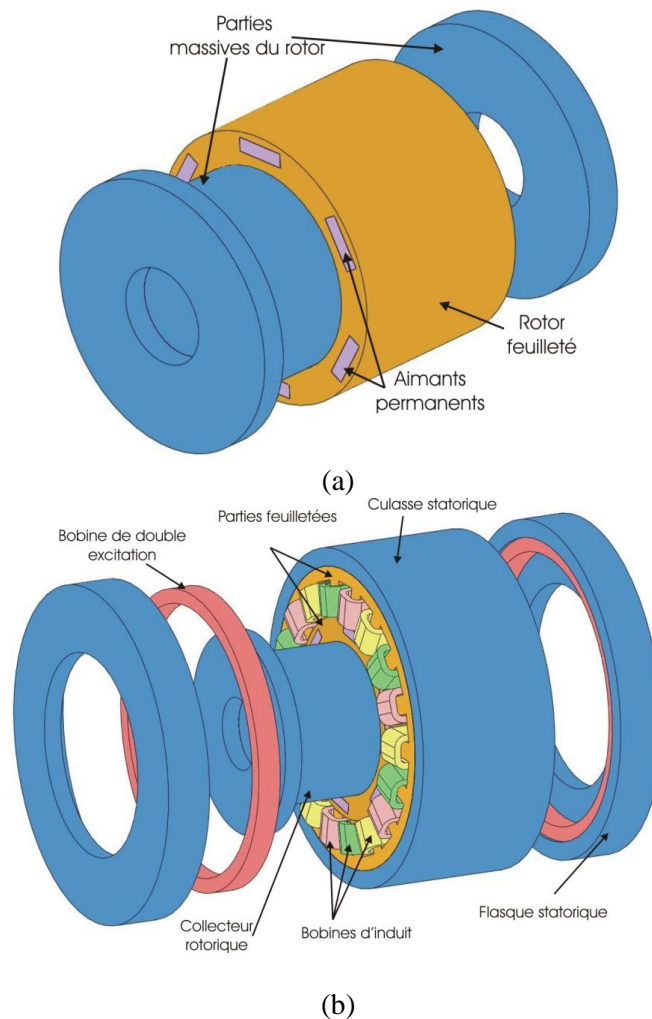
Composition de la machine à aimants enterrés(a) rotor à aimants et parties massives (b) vue éclatée de la machine.
